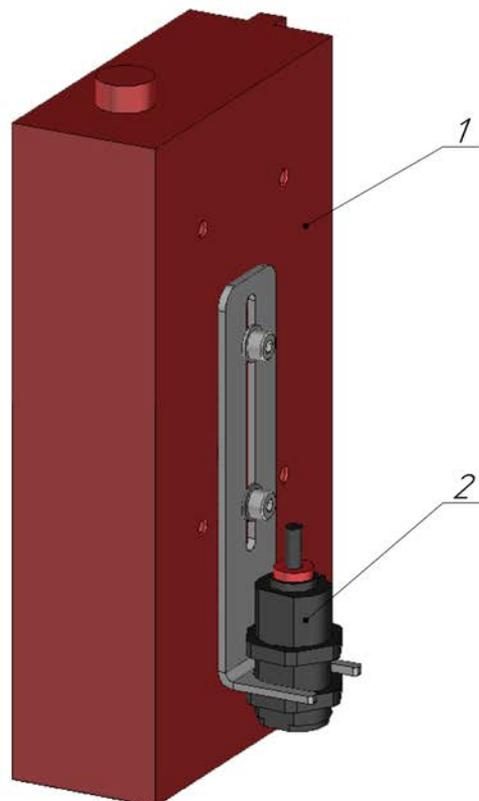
Вариант крепления фотодатчика. Условные обозначения: 1 — печатающая
